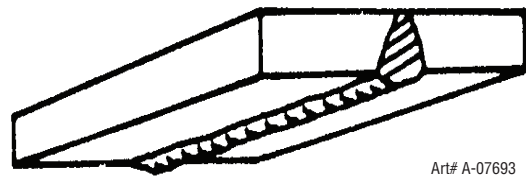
Position au plafond, soudure bout à bout
